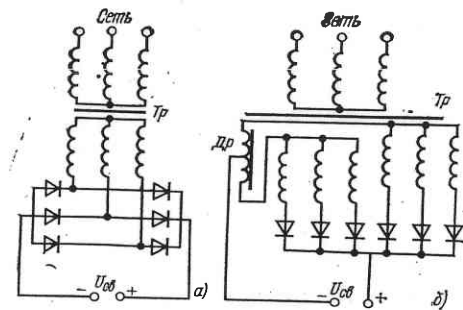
Принципиальные схемы сварочных выпрямителей:
